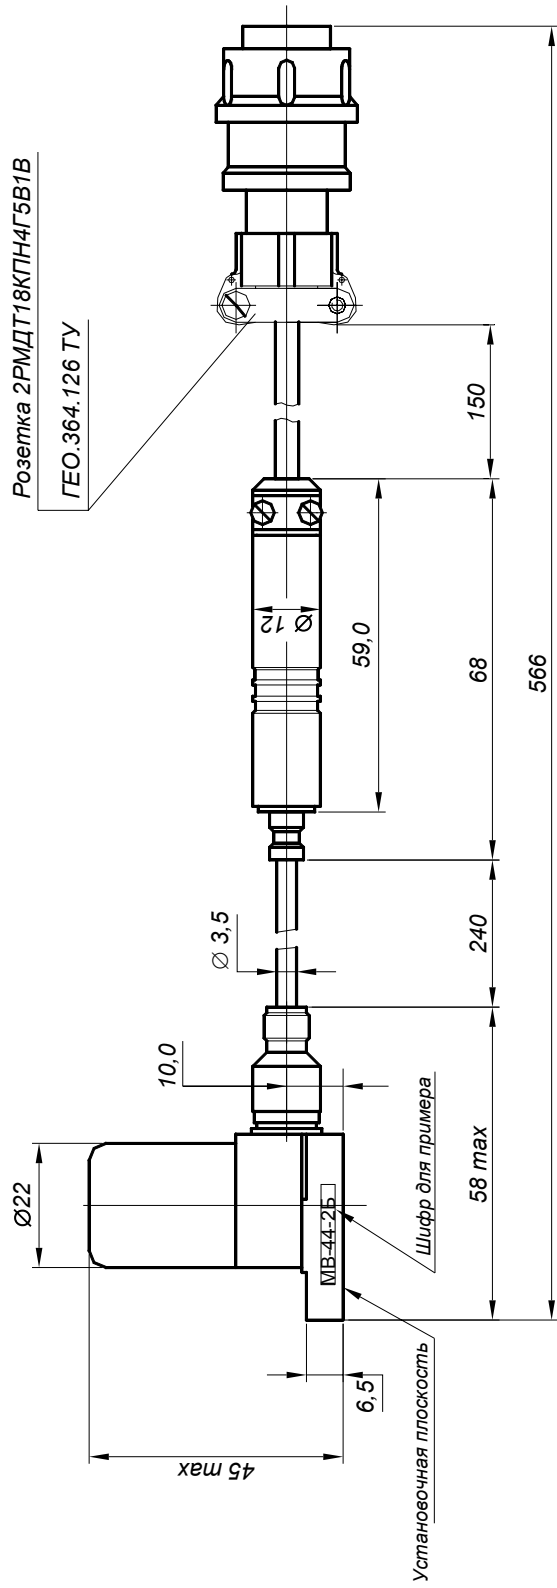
Габаритно-установочные размеры вибропреобразователя MB-44-2Б/0,24/0,15
